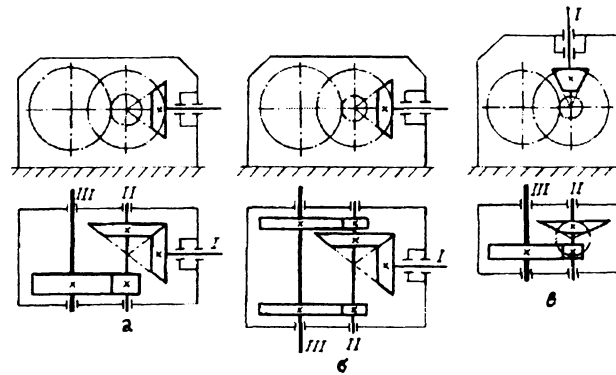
Кинематические схемы двухступенчатых коническо-цилиндрических редукторов:
